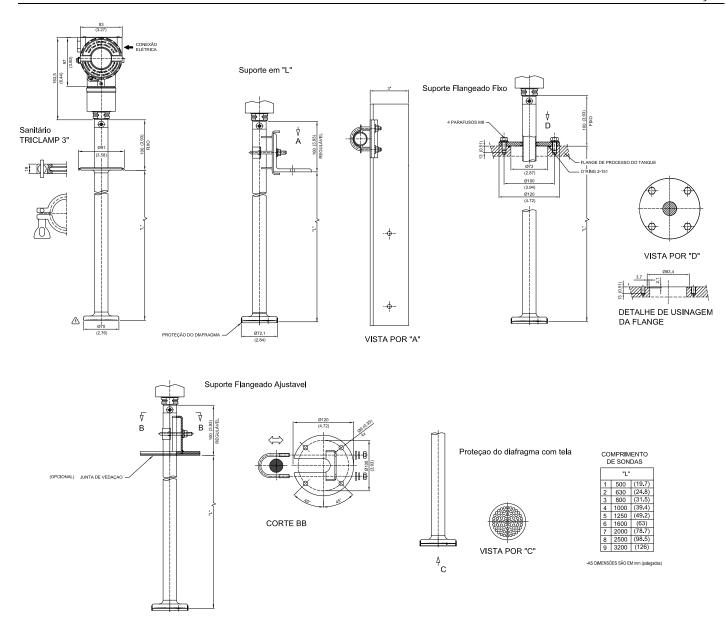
(d) - Desenho Dimensional de Montagem do LD290 - Nível (Inserção)
